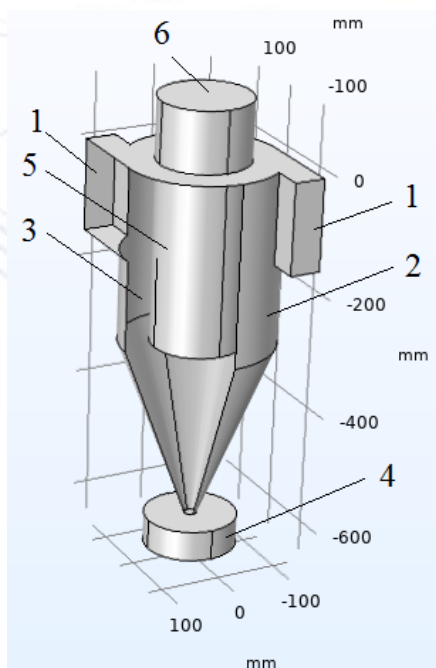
Классический центробежный пылеуловитель. 1-вход в спиральный воздухозаборник, 2- цилиндрический корпус пылеуловителя, 3- конусный корпус пылеуловителя, 4-бункер, 5- труба для отвода очищенного воздуха, 6-выход очищенного воздуха.
